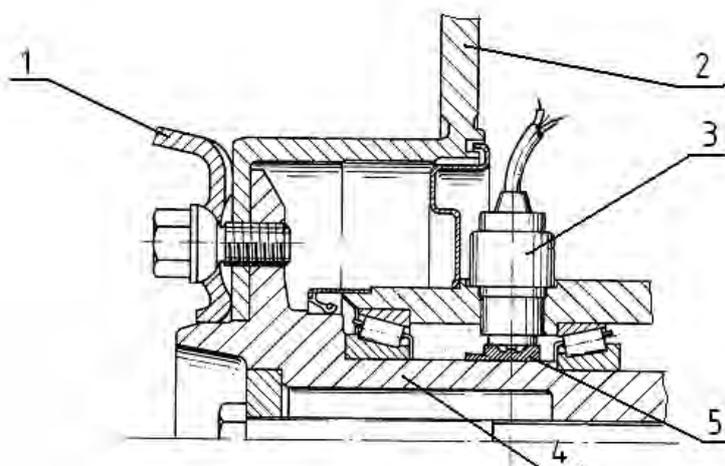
Схема установки датчика угловой скорости колеса [13]: 1 – колесный диск; 2 – тормозной диск; 3 – датчик частоты вращения колеса; 4 – ступица колеса; 5 – зубчатый ротор
